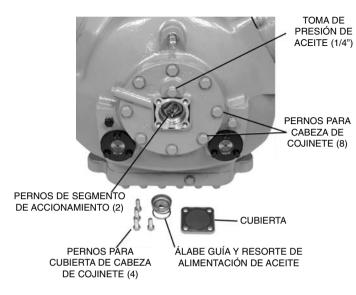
Cómo Retirar la Cabeza de Cojinete del Extremo de Bomba (Compresor 06E)
